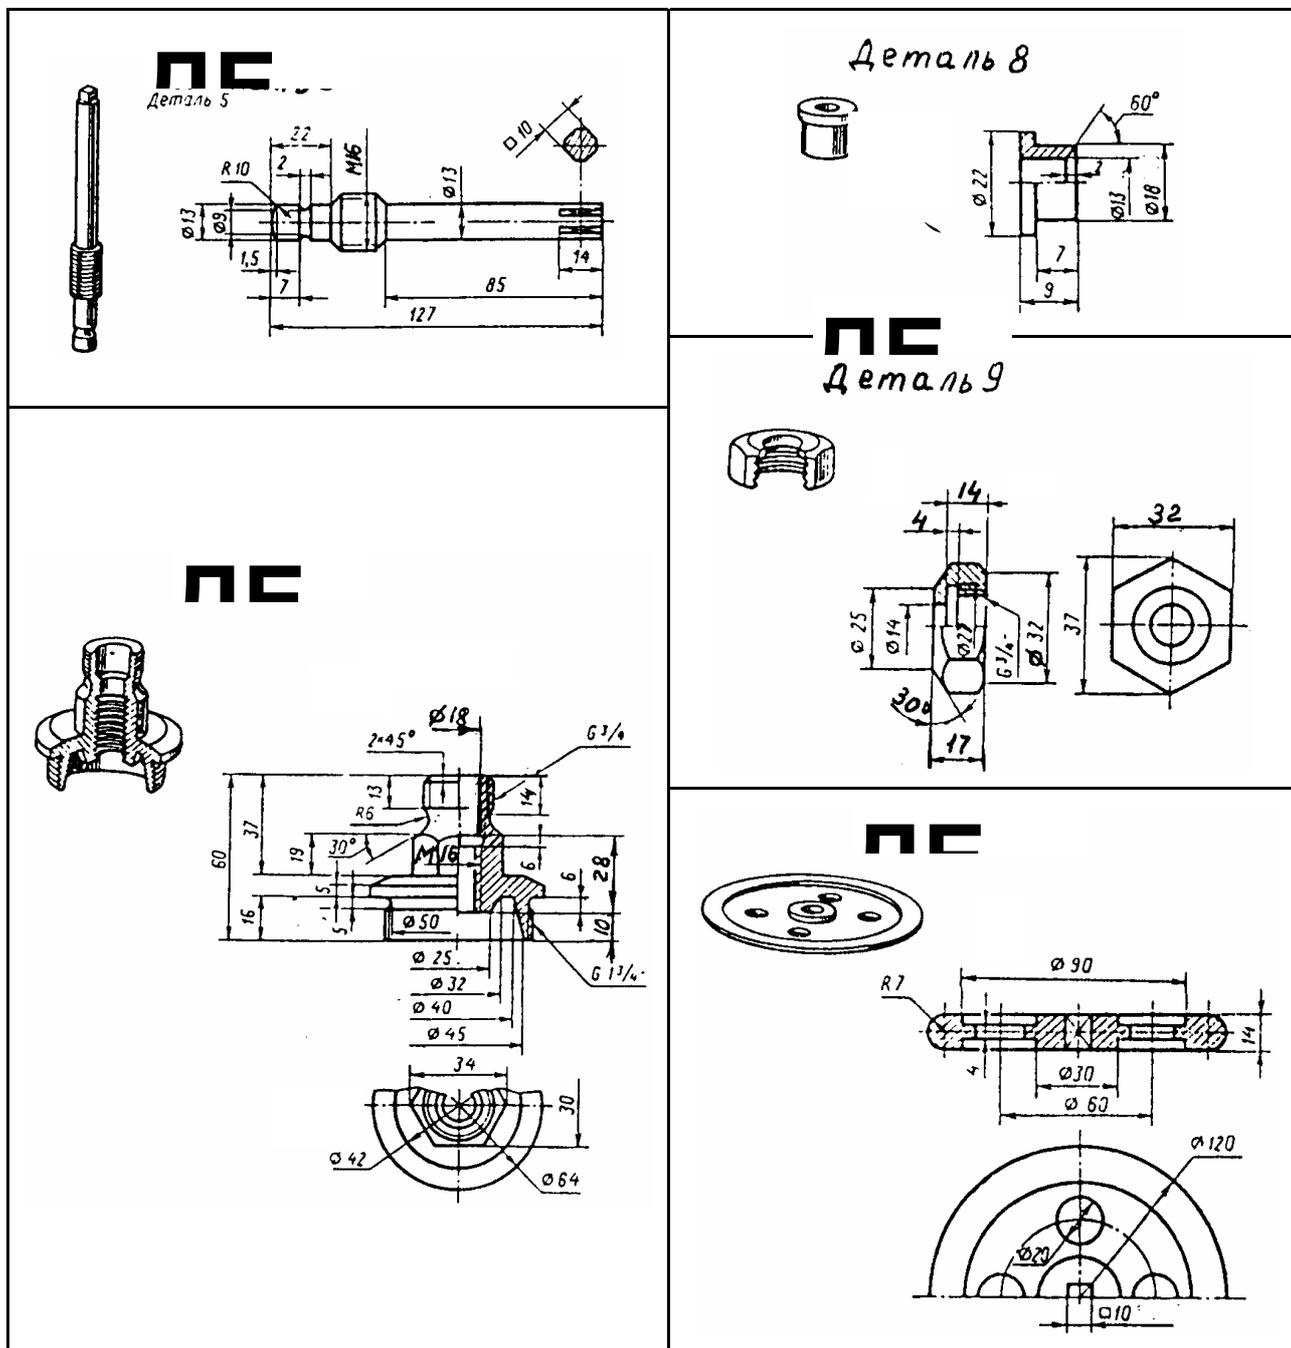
Эскизы деталей вентиля (рис.3. 64)
